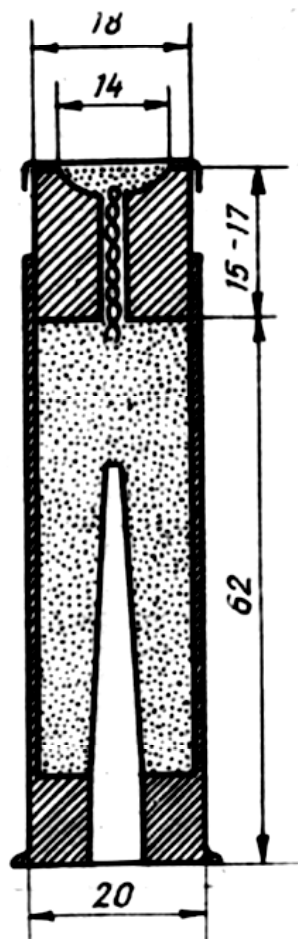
Ракетний двигун із затримкою порохового спалаху.
